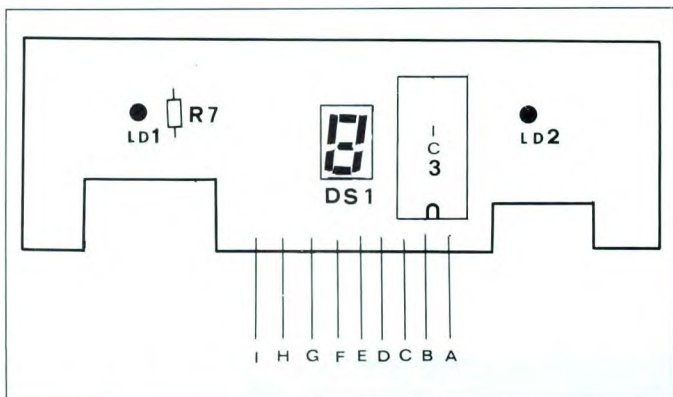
Disposizione dei componenti sulla basetta del display. Il circuito stampato va montato verticalmente rispetto a quello principale al quale rimarrà fissato rigidamente per mezzo dei collegamenti A-I.
